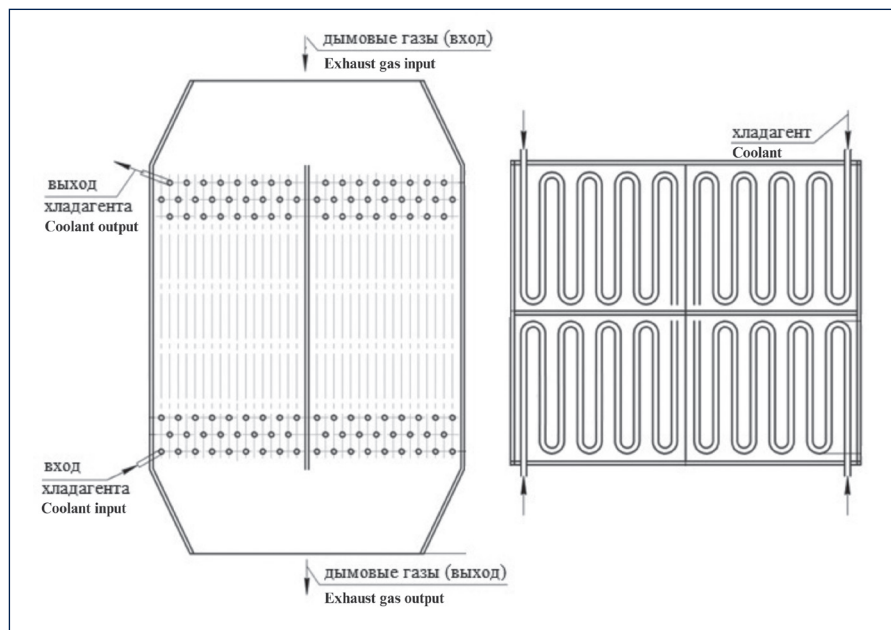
Схема котла-утилизатора типа трубчатых печей
